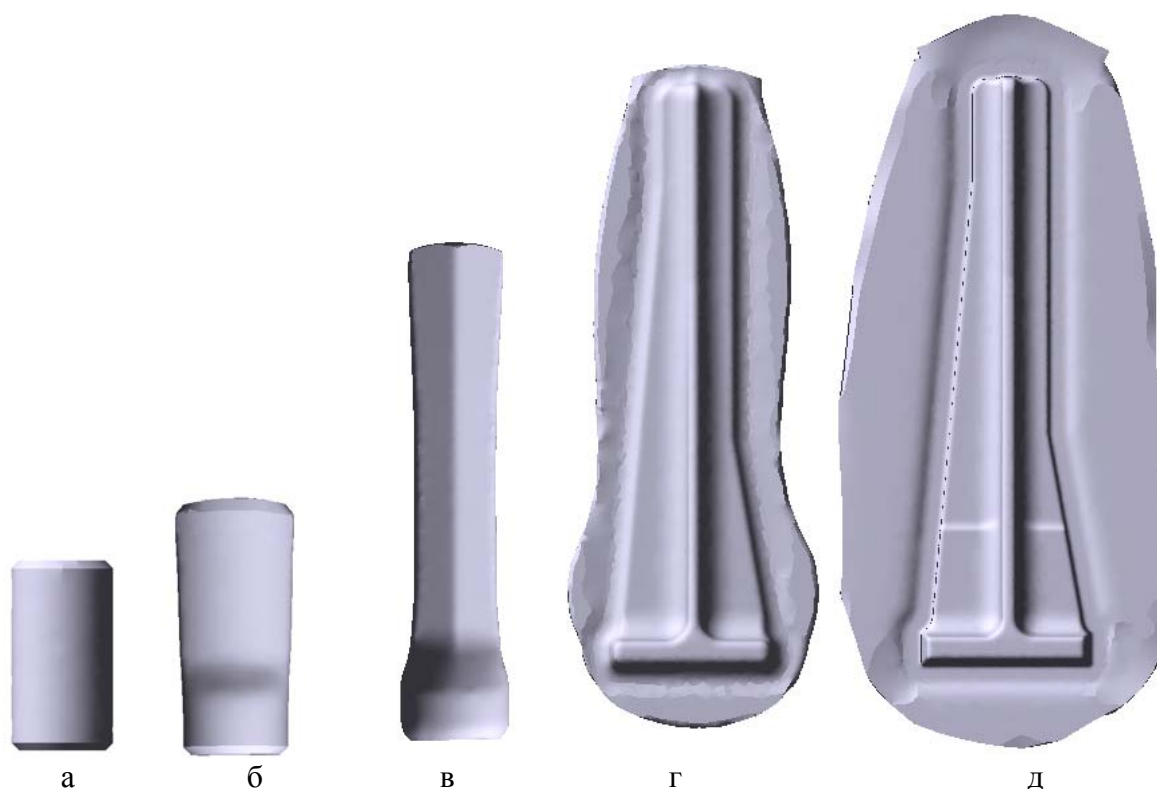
Штампованная поковка «фитинг», полученная из мерной заготовки с применением процесса вальцовки и подготовительного ручья:
